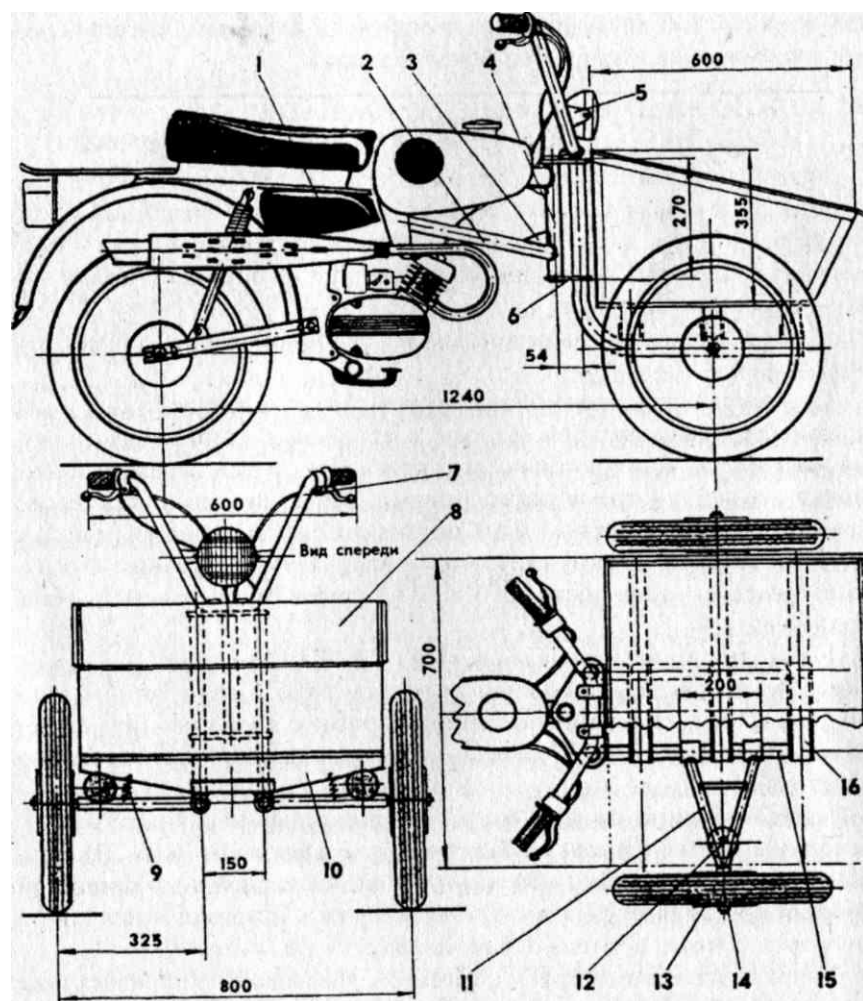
Конструкция грузового мопеда на базе мокика "Карпаты": 1 - мокик; 2 - подкос; 3 - косынка; 4 - рулевая колонка (труба, диаметр которой равен диаметру рулевой колонки); 5 - кронштейн крепления фары; 6 - мостики рулевой колонки; 7 - руль (штатный или самодельный ИЗ трубы диаметром 22х2 мм); 8 - кузов; 9 - возвратная пружина; 10 - поперечина (3 шт., сосновая доска сечением 40х80 мм); 11 - качалка подвески; 12 - амортизатор; 13 - передние колеса; 14 - гайка крепления колеса; 15 - основание грузового блока; 16 - ложементы поперечин
